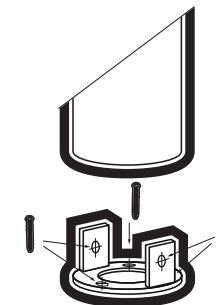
Схема крепления светильника PGB 04-800 к опорной поверхности
